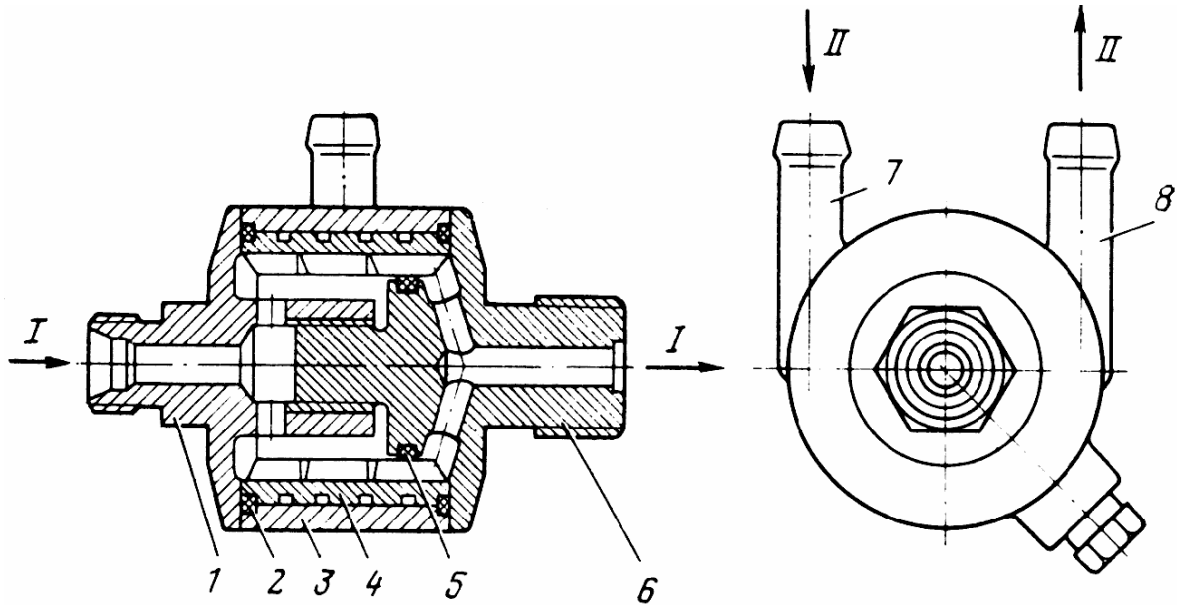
Подогреватель газа газодизельных автомобилей КамАЗ: I и II - направления движения газа и воды; 1 - штуцер входной; 2, 5 - кольца уплотнительные; 3 - корпус нагревателя; 4 - элемент теплообменный; 6 - штуцер выходной; 7 - патрубок подвода охлаждающей жидкости; 8 - патрубок слива охлаждающей жидкости в коробку термостата
